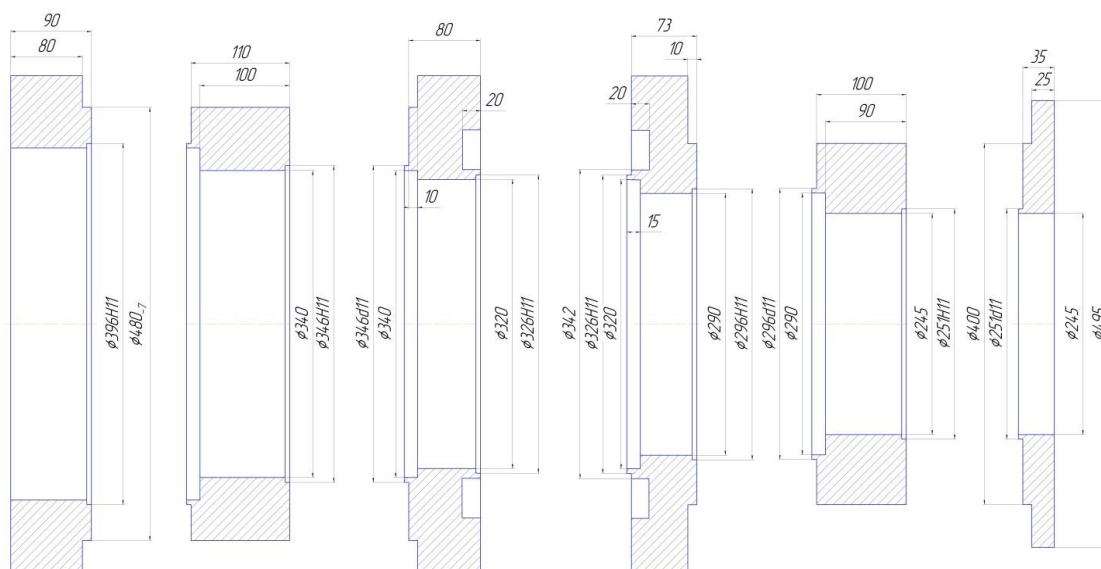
Набор раскатных колец для изготовления сварной заготовки шпангоута (Этап №1)
